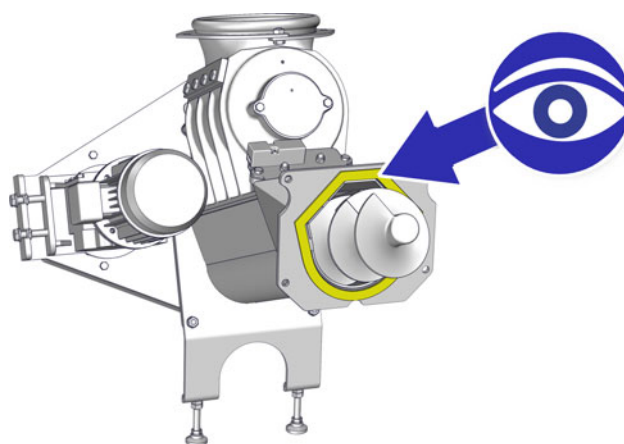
Joint d'étanchéité sur la bride de la vis d'alimentation
